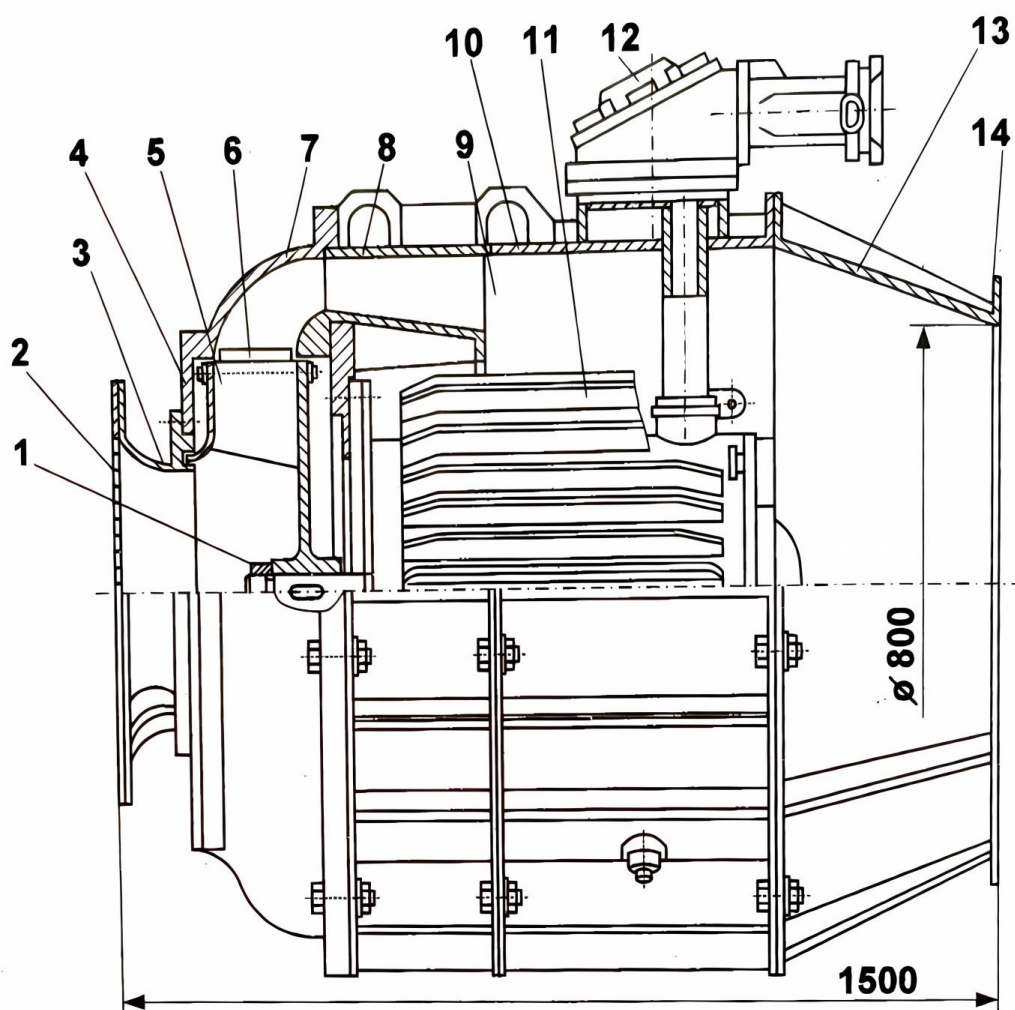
Вентилятор местного проветривания ВЦ-7: 1 – стопорная гайка; 2 – защитная решетка; 3 – входной патрубок с коллектором; 4 – фланец крепления выходного коллектора; 5 – рабочее колесо с лопатками; 6 – закрылок; 7 – отвод; 8 – передняя часть корпуса; 9 – лопатки спрямляющего аппарата; 10 – задняя часть корпуса; 11 – электродвигатель; 12 – кабельный ввод; 13 – выходной конический патрубок; 14 – фланец для присоединения воздуховода
